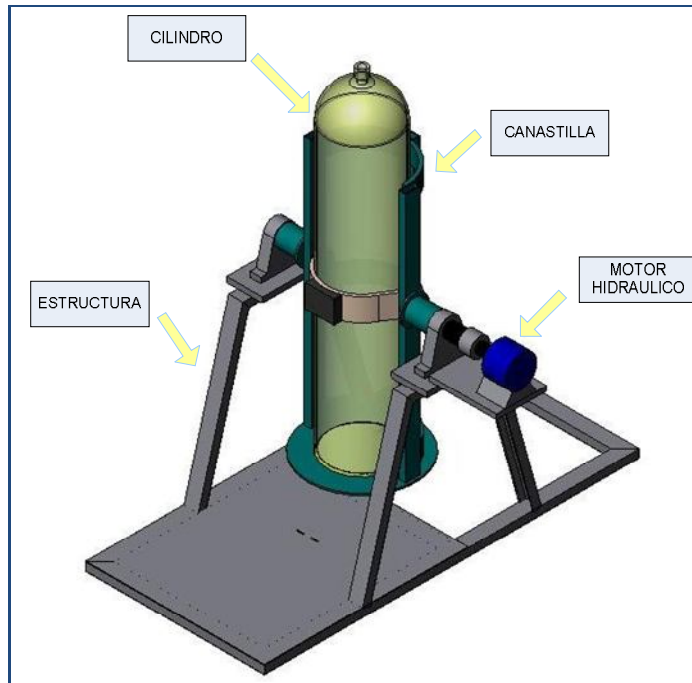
Diseño de la máquina con rotación de 360 grados y motor hidráulico
